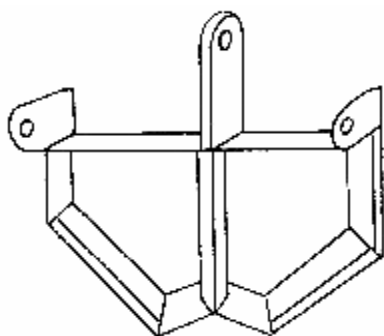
Рабочий орган глубокорыхлителя РГ-
